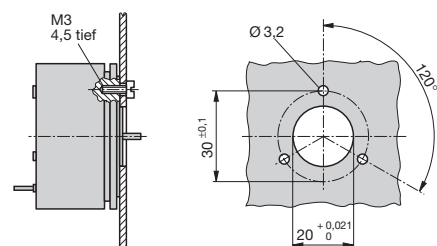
Bohrplan für Befestigung mit 3 Zylinderschrauben M3.
